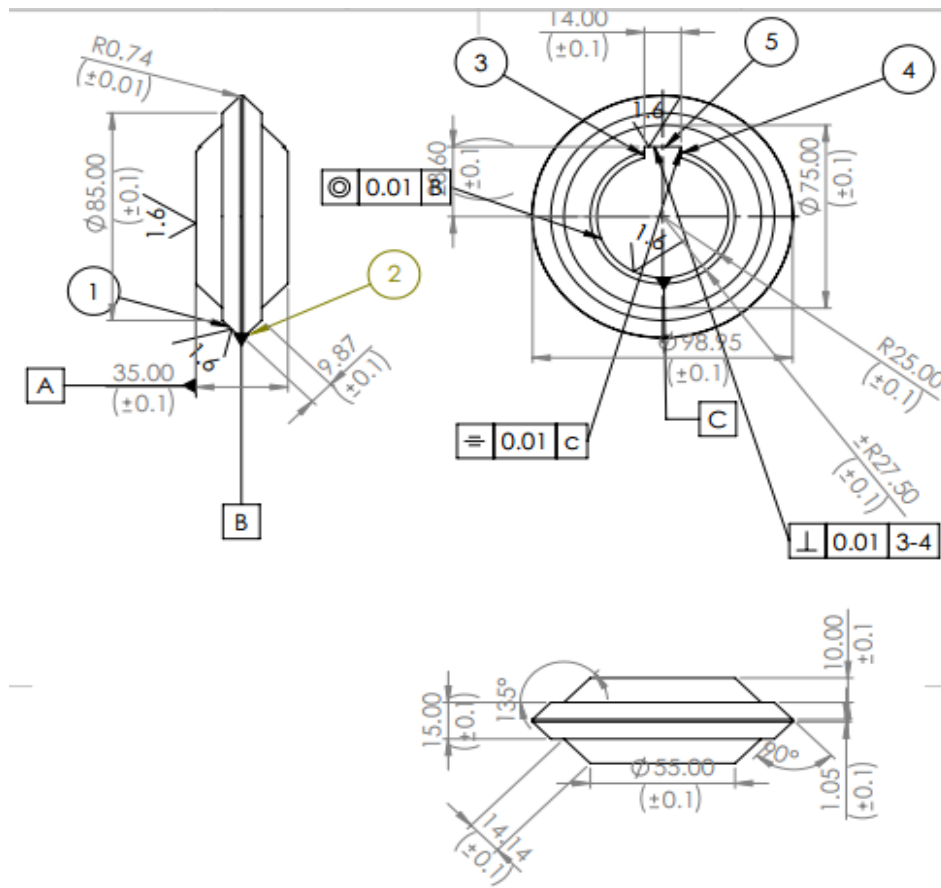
dessin de définition de galet supérieur (Passe 12)
